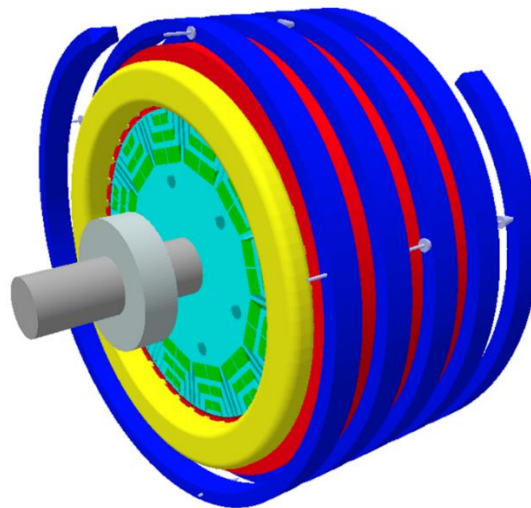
Vue en trois dimensions de la machine synchronélectrique montrant la chemise d'eau en spirale
